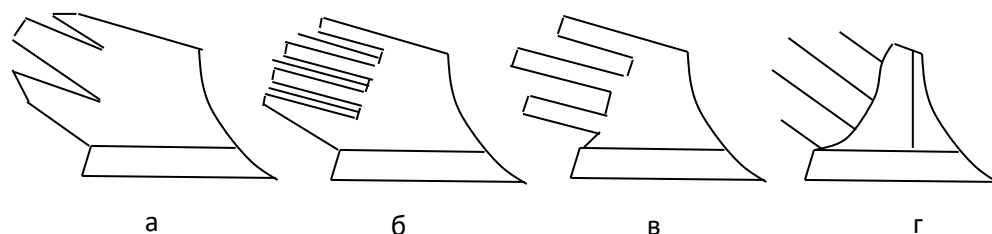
Корпуса с различными отвальными поверхностями
